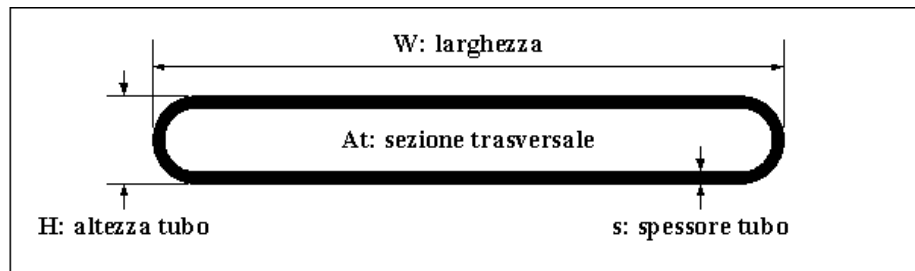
principali caratteristiche geometriche nella sezione trasversale di un tubo piatto semplice
